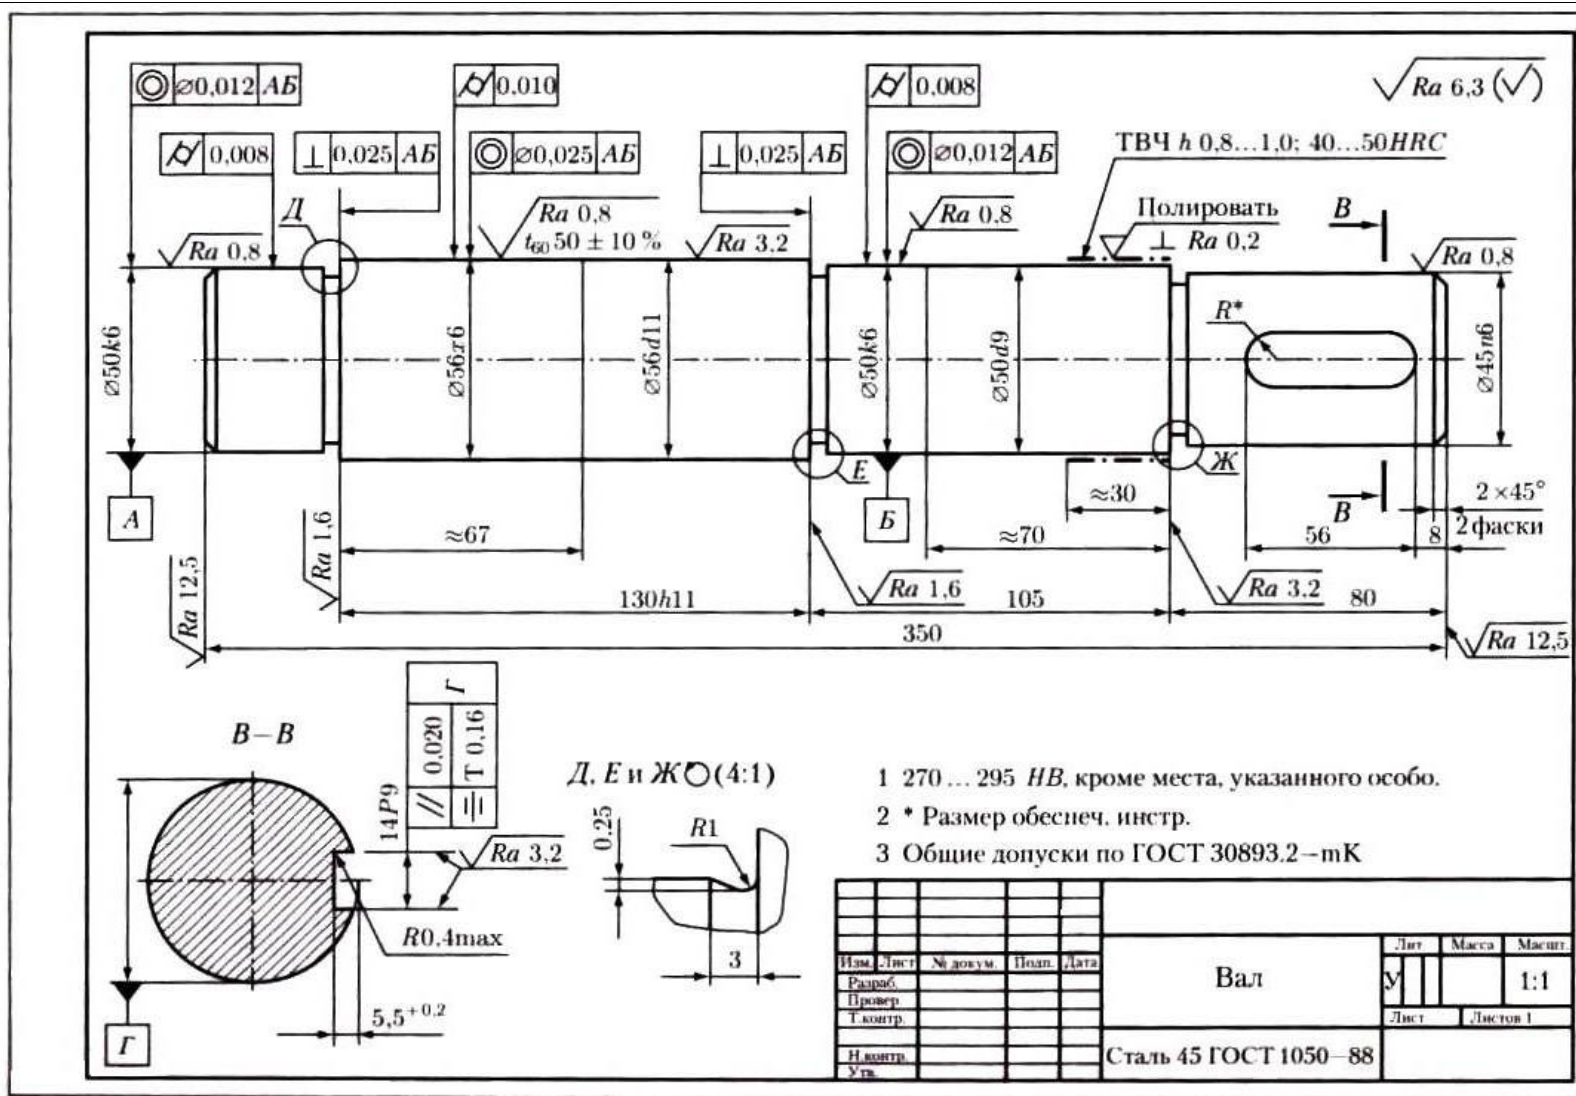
Пример рабочего чертежа вала редуктора
